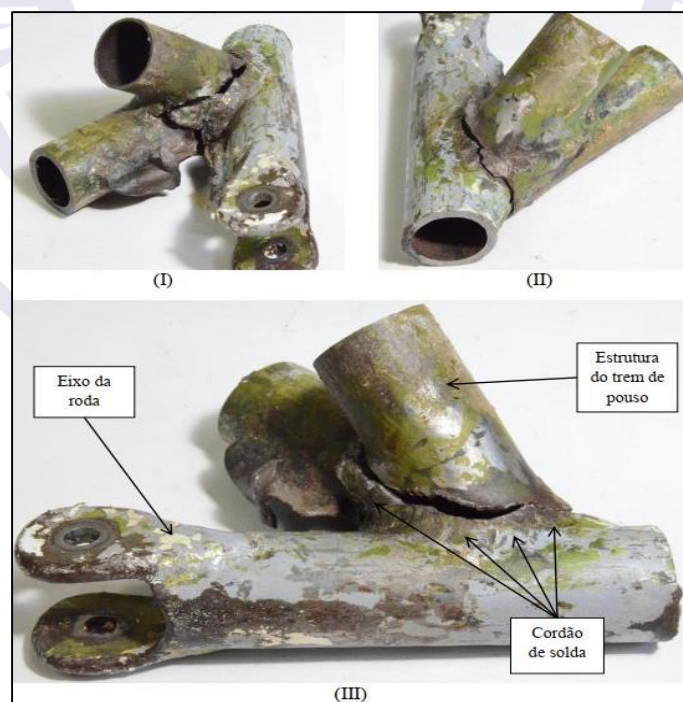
Em (I-III), sobreposição das superfícies de fratura. Nota-se que a fratura se deu ao longo do cordão de solda que unia a estrutura do trem de pouso ao eixo da roda.
